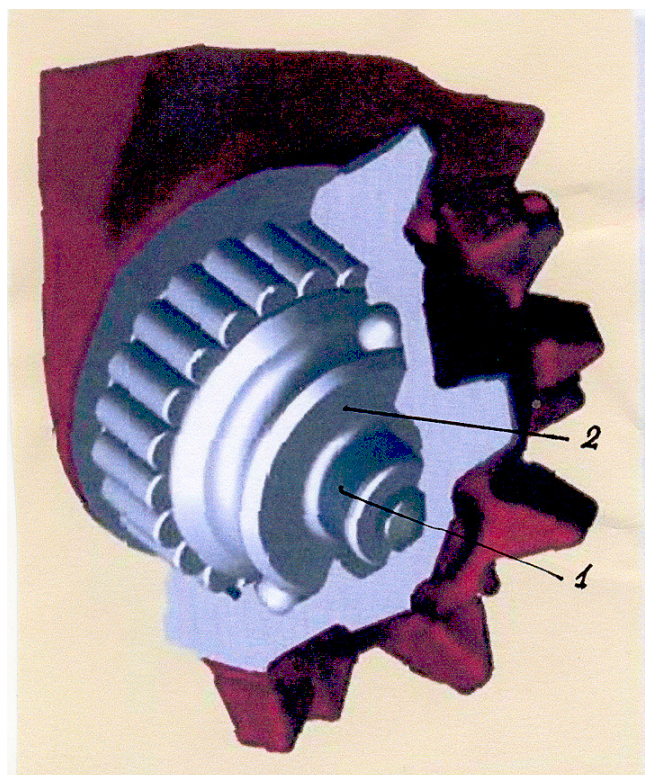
Опора открытая с двумя подшипниками качения
